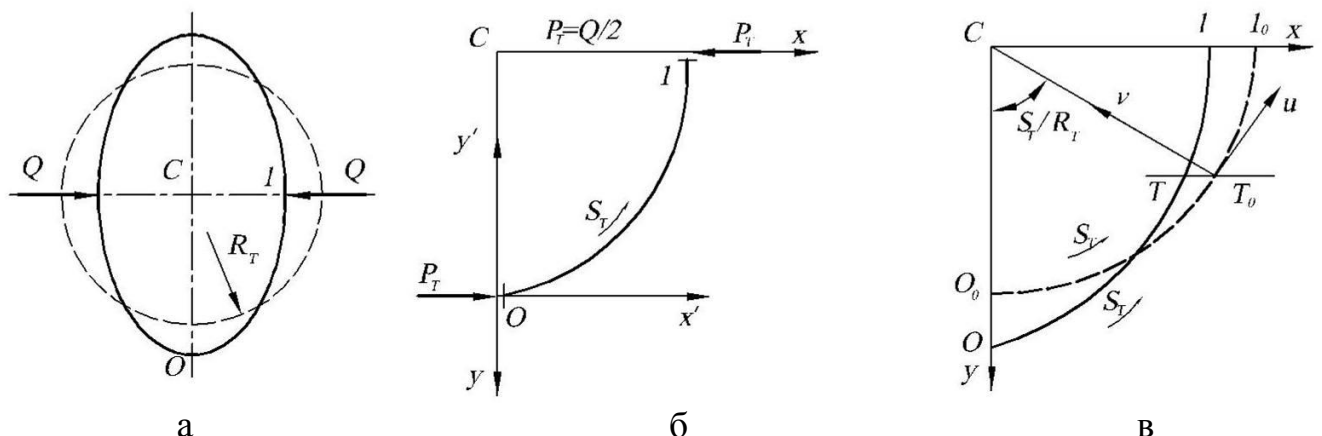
Розрахункові схеми для визначення еліптичних параметрів деформованої заготовки: C – центр заготовки; O – точка перегину
